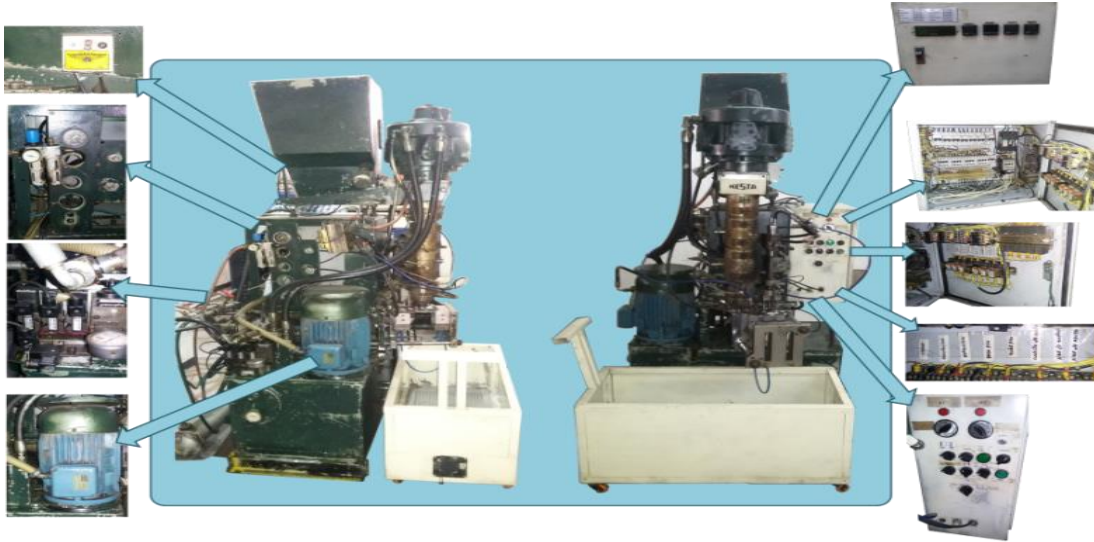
Gabinete de la sopladora Bekum. Fuente: propia, Junio de 2016.
